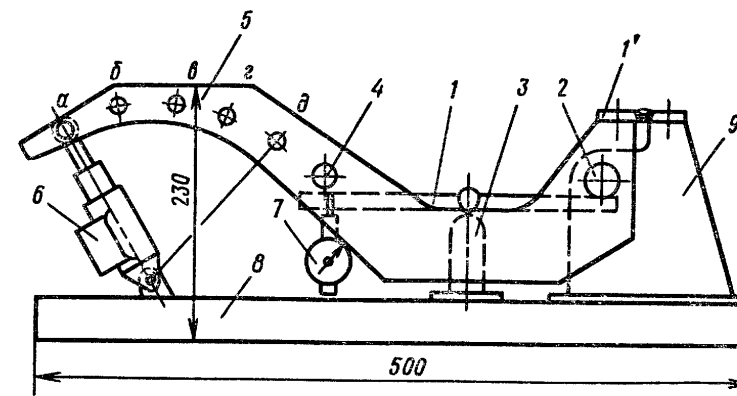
Схема переносной малогабаритной машины ЛТП-11 для оценки технологической прочности при лучевых способах сварки:
